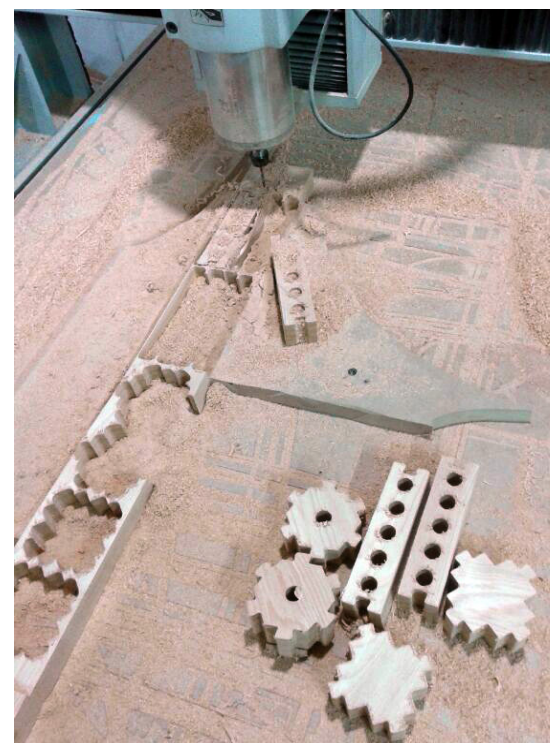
Detalle durante el frezado de las piezas estructurales
